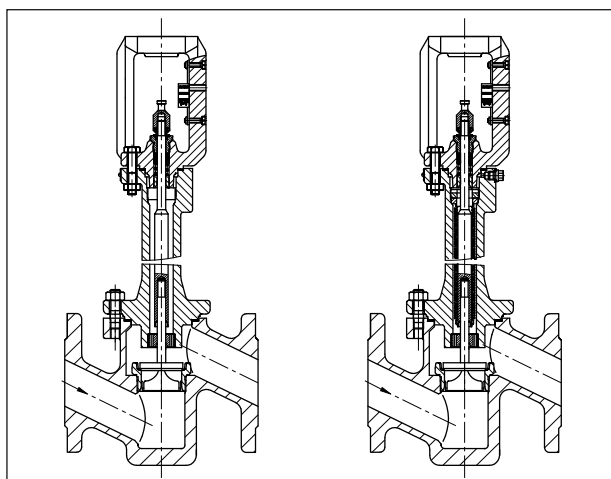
Ventil Typ 3241 · DN 15 bis 80 · Schmiedestahlausführung · links: mit Isolierteil, rechts: mit Balgteilabdichtung
